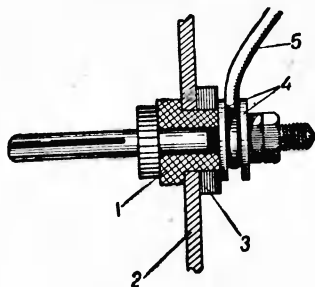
Изолирование выводного контакта от металлического корпуса прибора:
